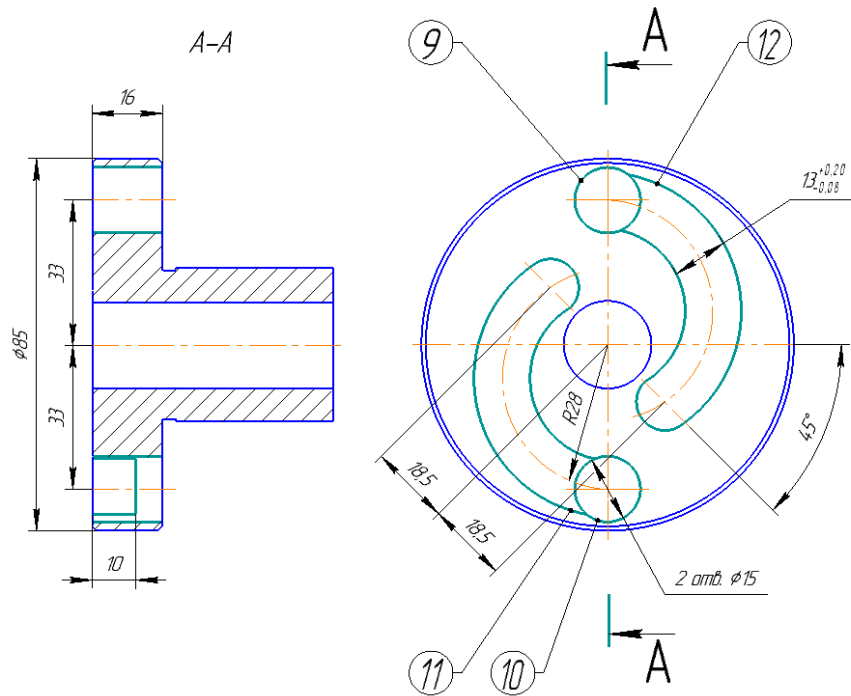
Ескіз обробки на операцію 040 Фрезерна з ЧПК
